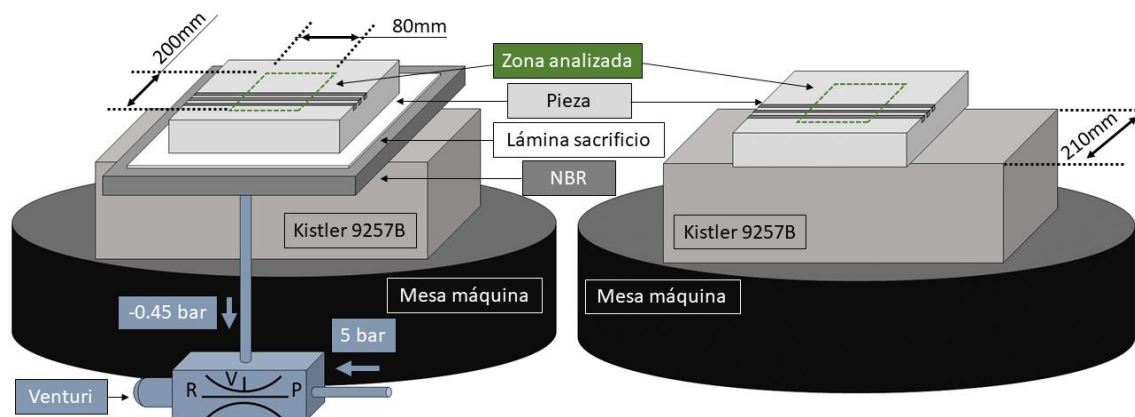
Esquema del banco de ensayo de ranurado con (izda.) y sin (dcha.) utilaje flexible.
